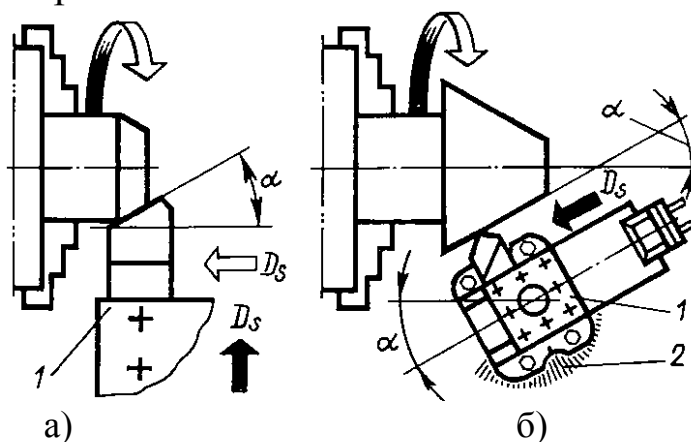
Схемы точения конической поверхности: а – широким резцом; б – поворотом верхних салазок суппорта с резцедержателем
